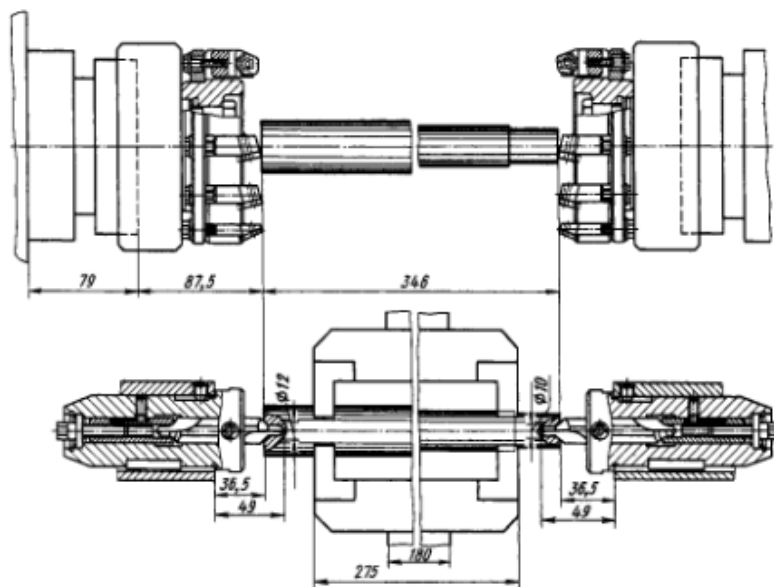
Обработка на фрезерно-центровальном станке
